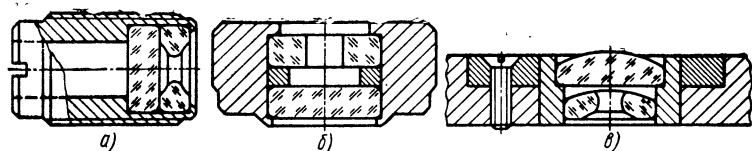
Неразборные конструкции цилиндрических закрытых опор
